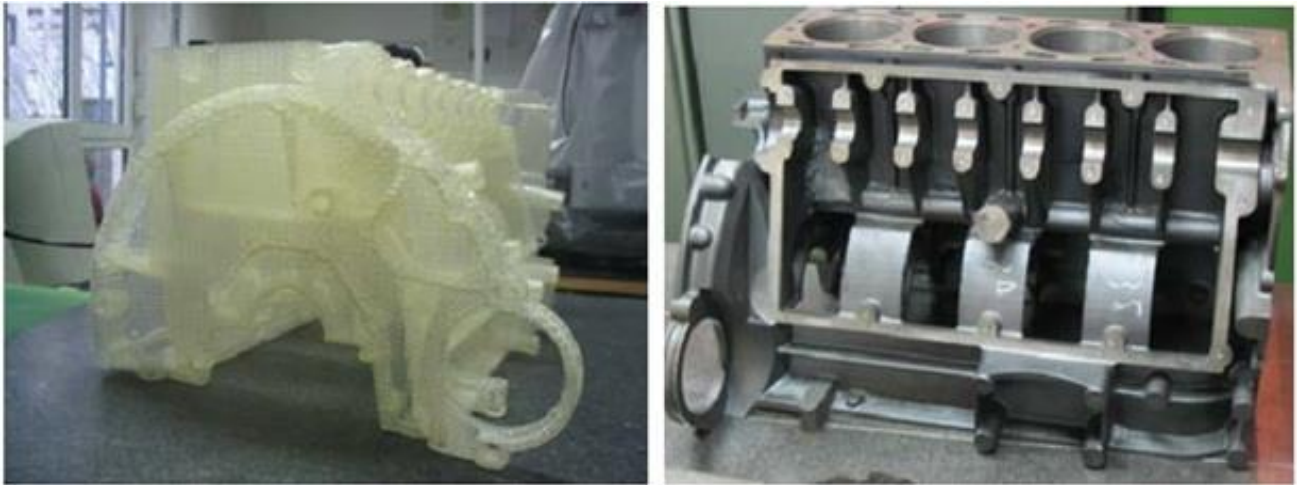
Quick-Cast модель и отливка блока цилиндров (чугун)
